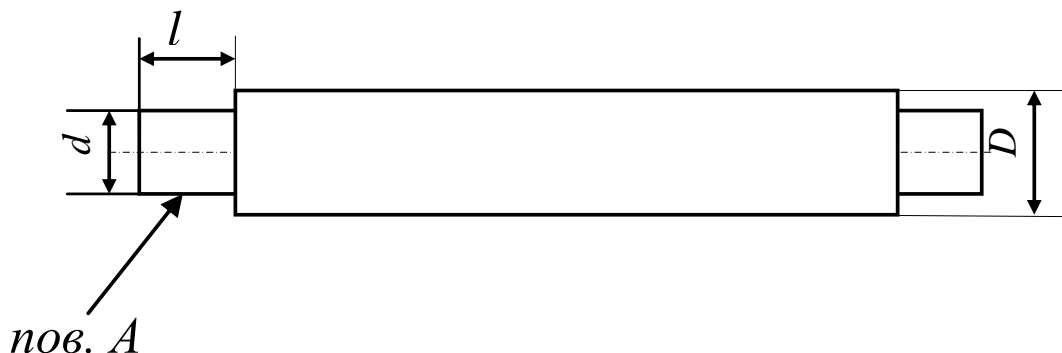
Ескіз деталі після наплавлення (поставити розмір $d = ?$)
